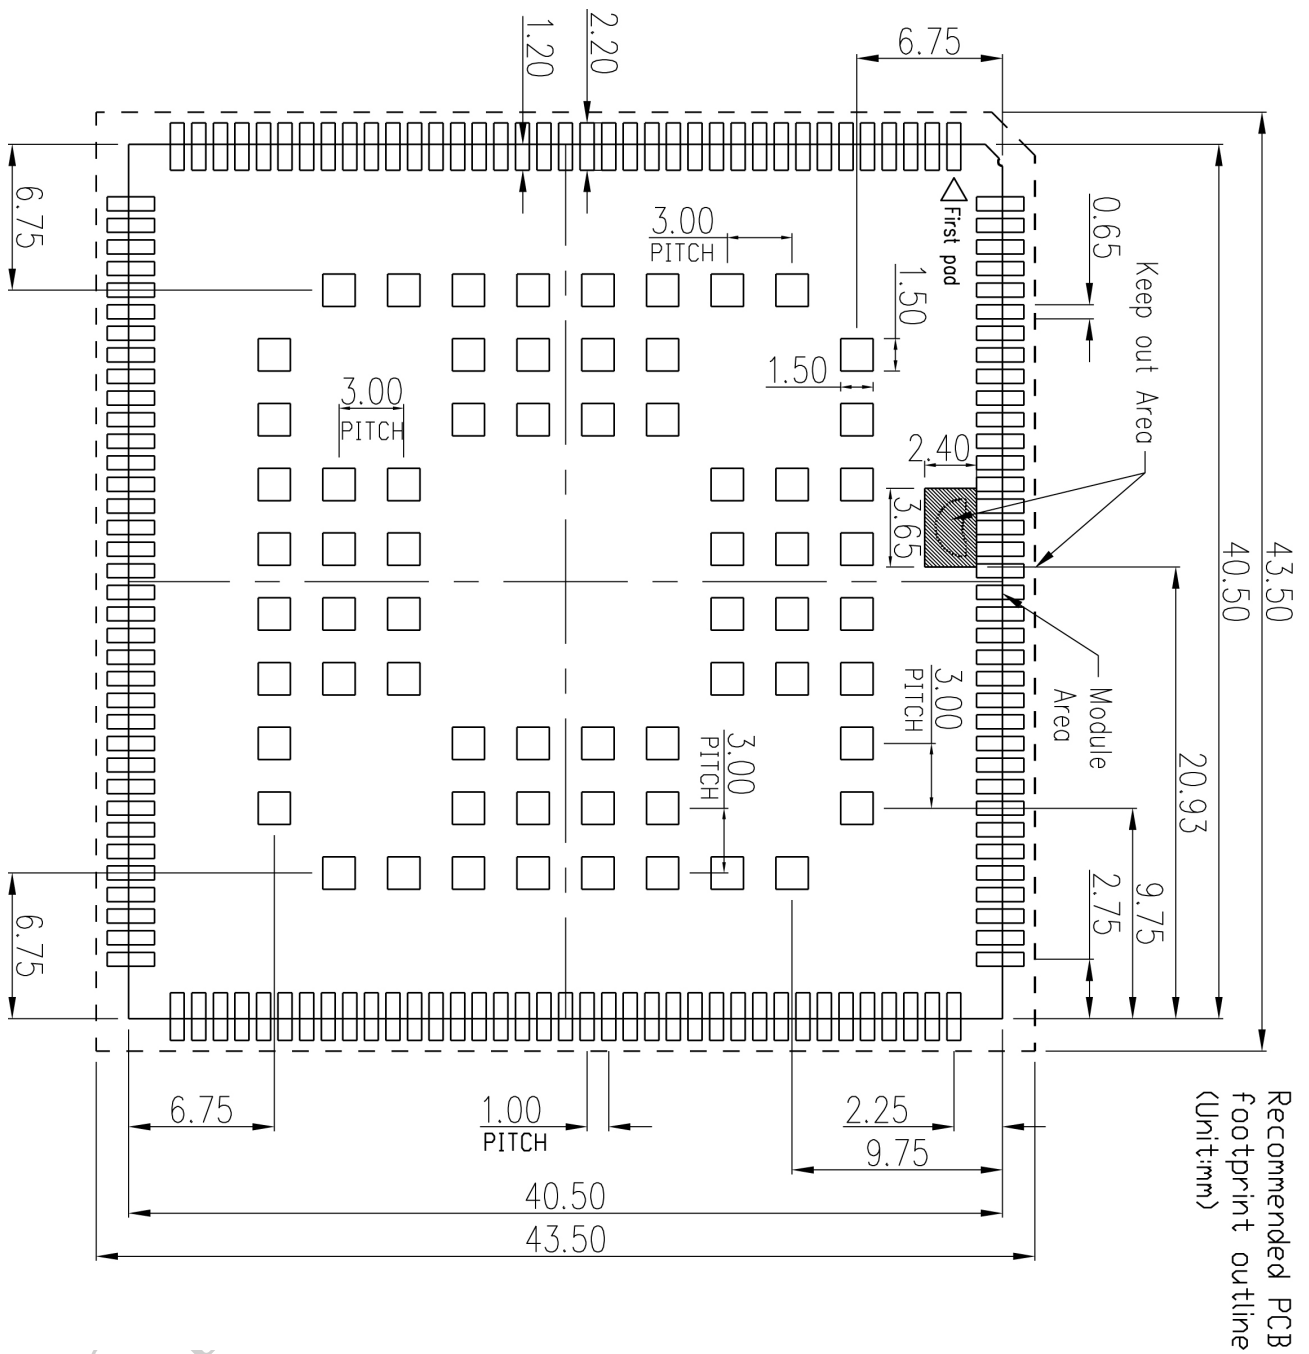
推荐 PCB 封装尺寸 (单位: mm)
